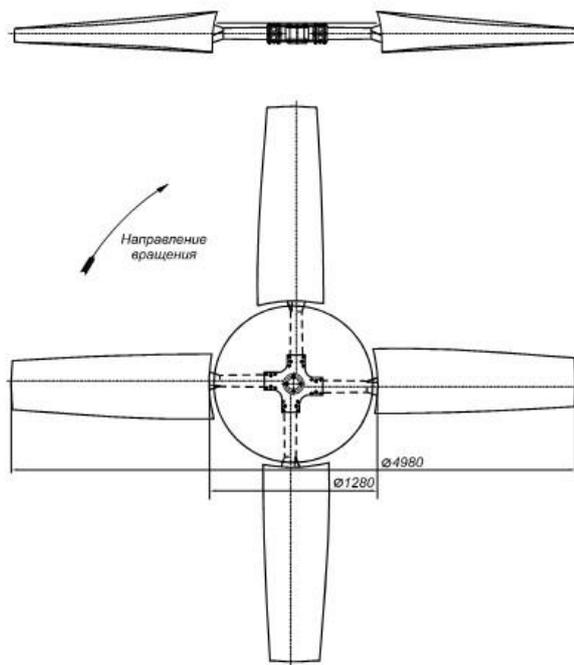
Рабочее колесо ГАЦ-50-4М2
